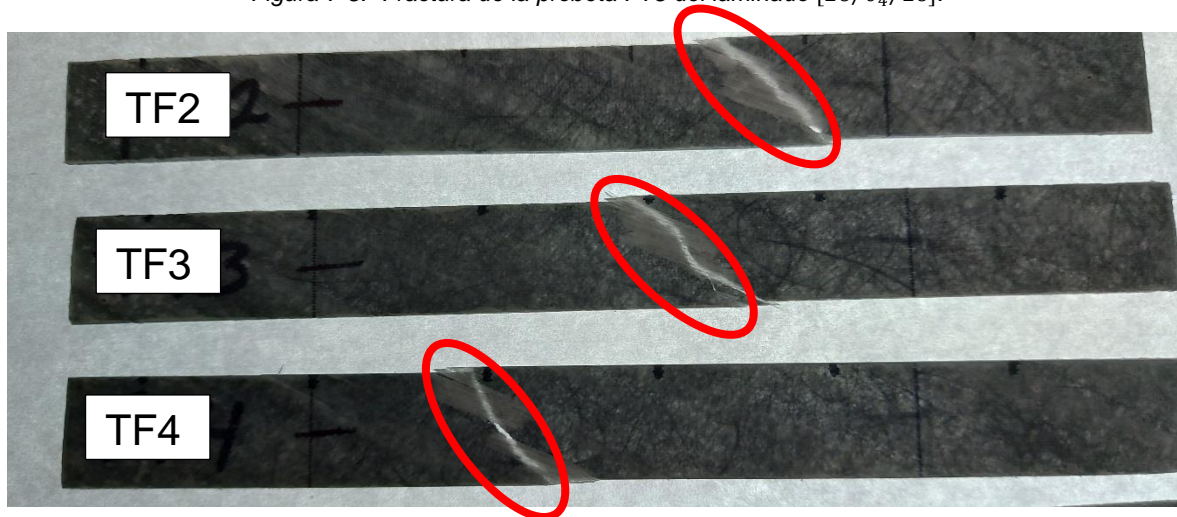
Fractura de la probeta FT2, FT3 y FT4 del laminado [26/0₄/26].
